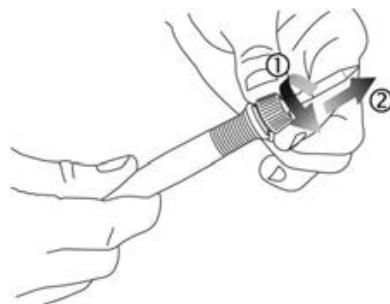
Desbloqueie a ponta de soldadura [1] e remova-a [2]
